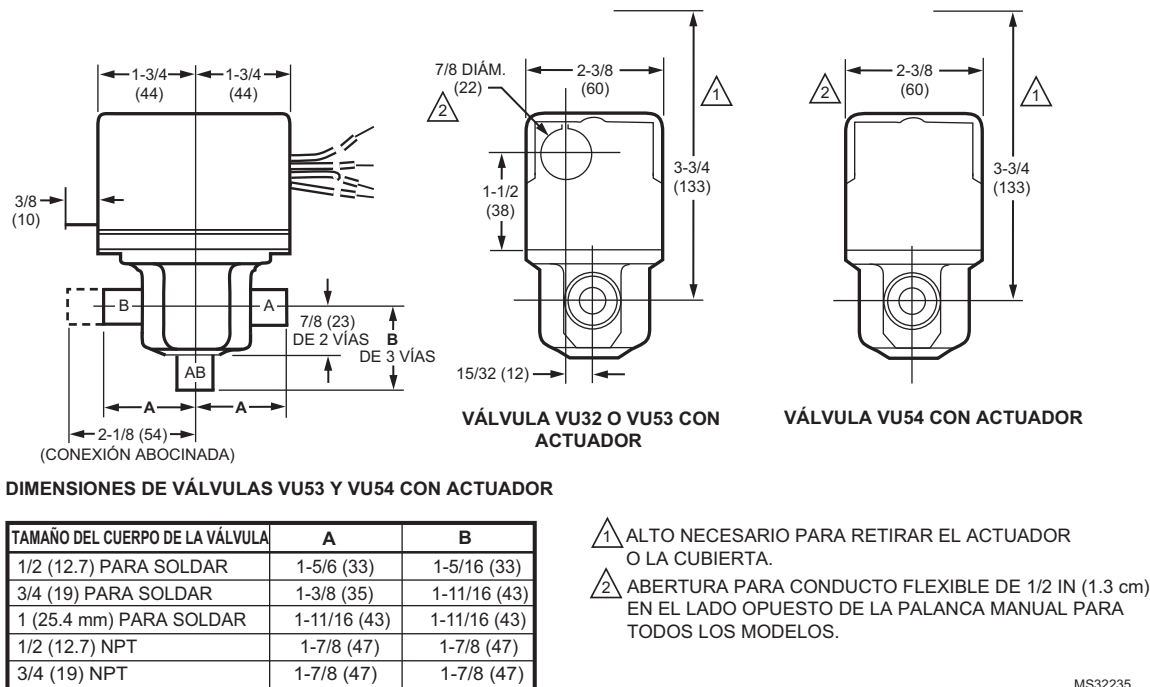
Dimensiones del montaje en pulgadas (mm).
